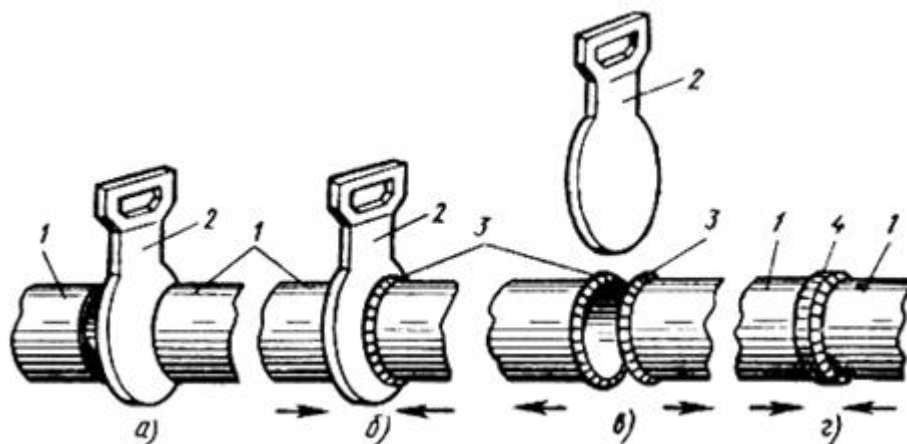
Технологическая последовательность соединения пластмассовых труб контактной стыковой сваркой:
